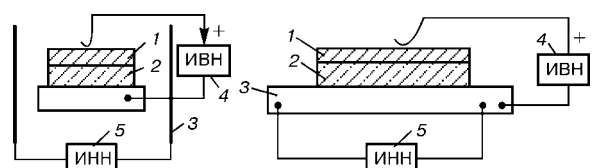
Принципиальные схемы ЭХС: 1 — стекло; 2 — кремний (металл); 3 — нагреватель; 4, 5 — источники сварочного напряжения соответственно низкого и высокого
